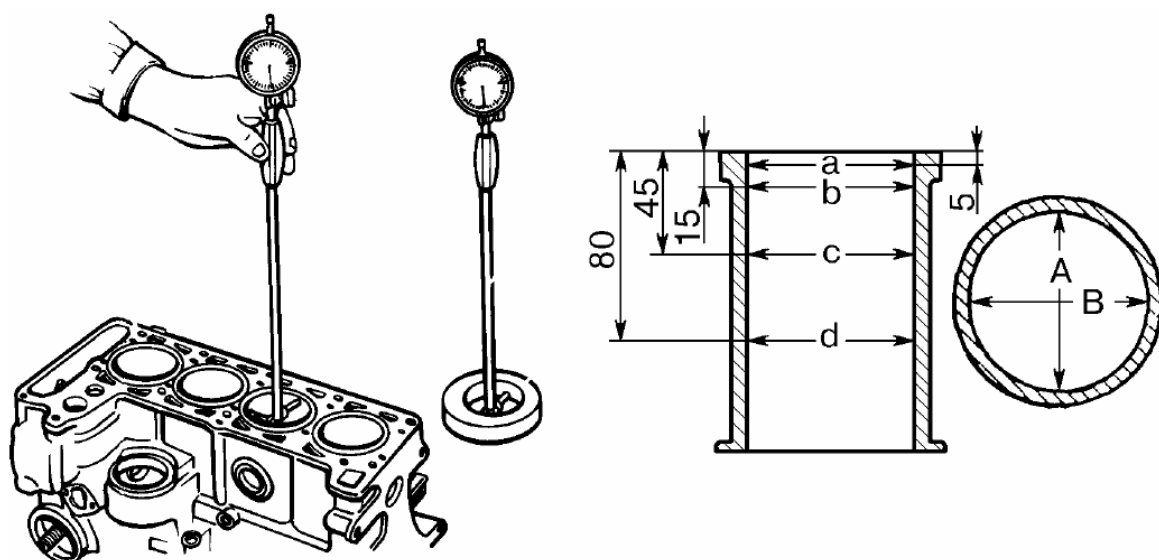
Контроль размеров цилиндра блока ВАЗ
